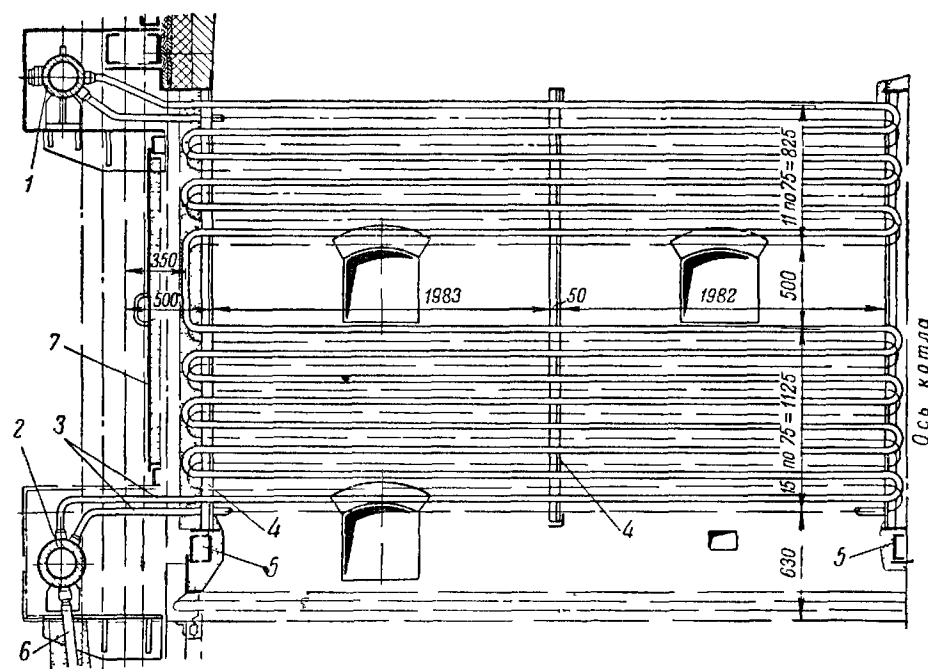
Левый верхний пакет экономайзера котла ТП-170-1.
